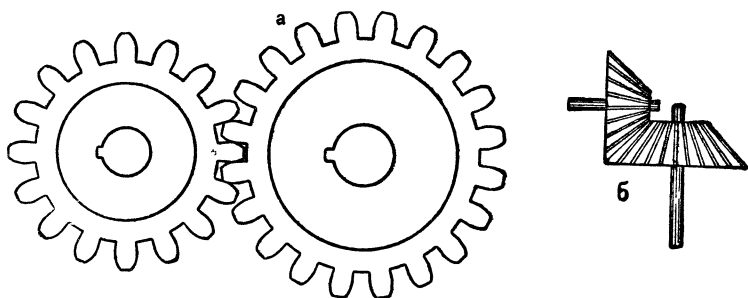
Зубчатая передача: а — цилиндрическая, б — коническая.
